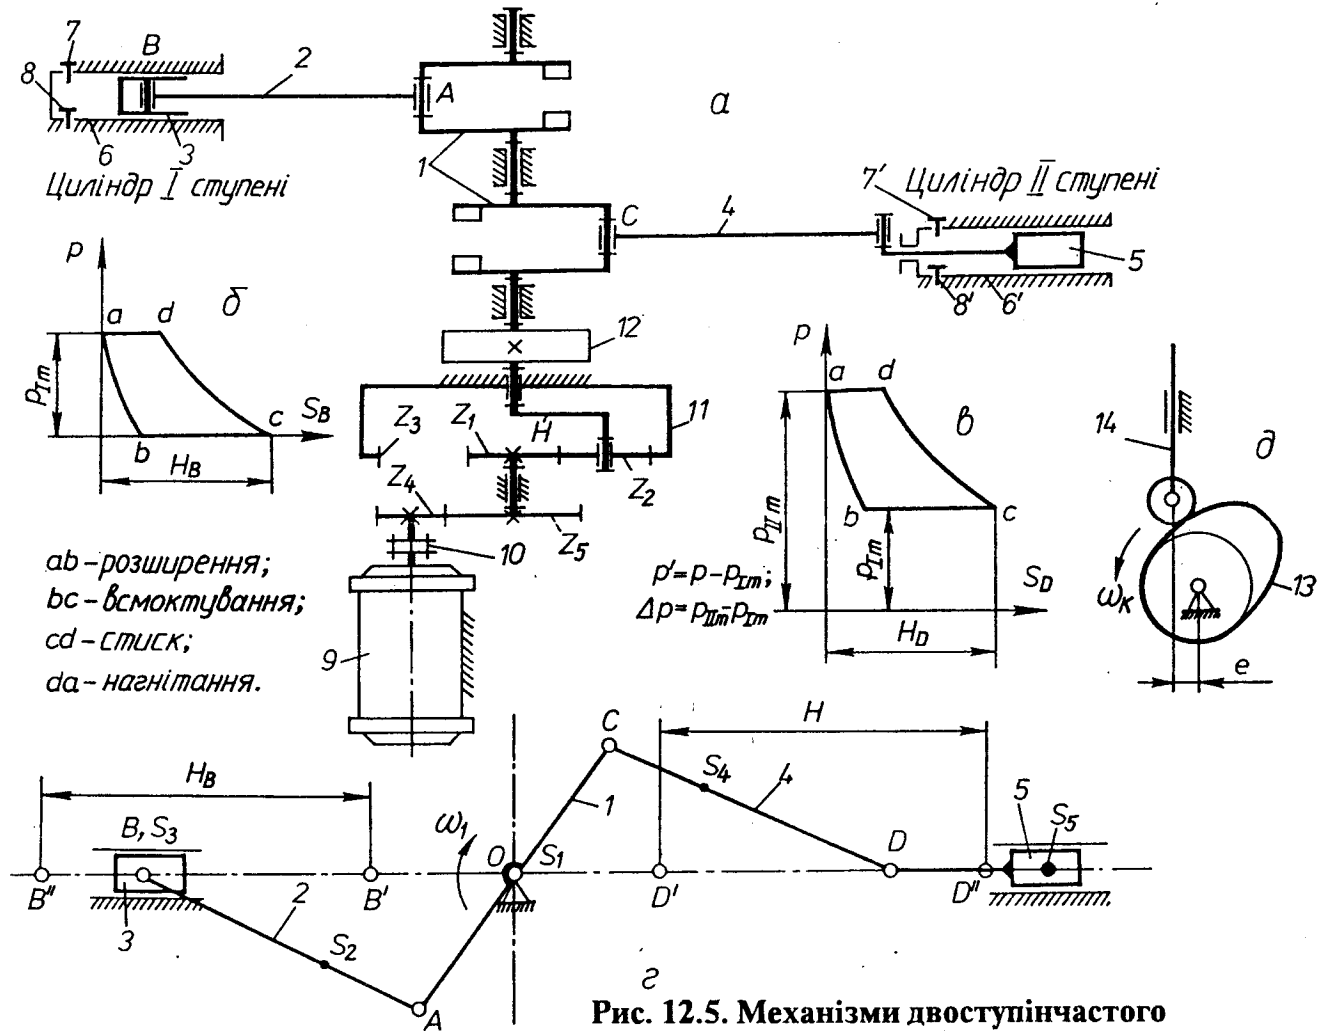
Механізми двоступінчастого двоциліндрового поршневого компресора :
